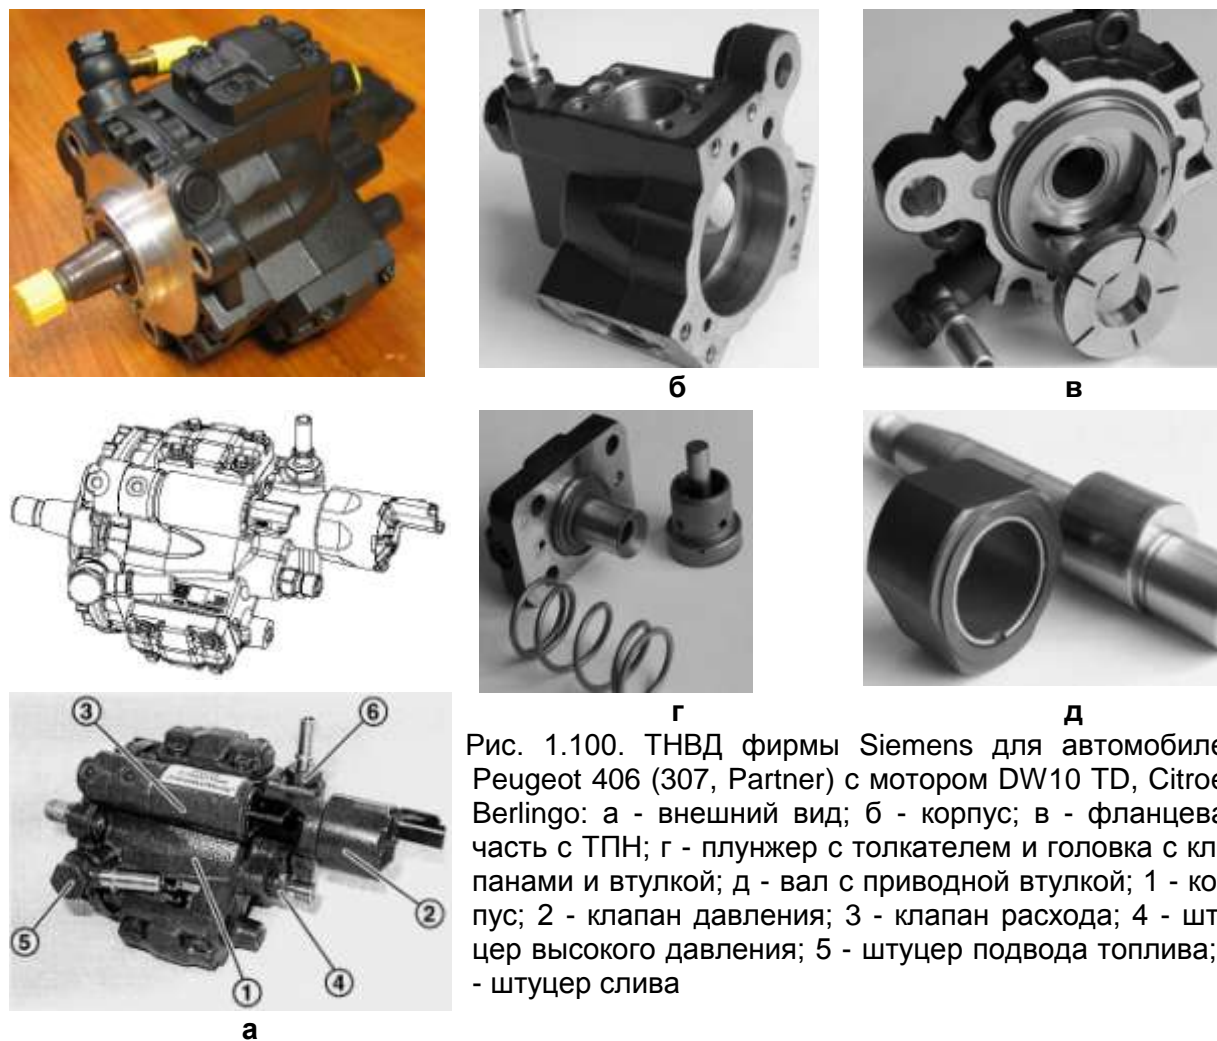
ТНВД фирмы Siemens для автомобилей Peugeot 406 (307, Partner) с мотором DW10 TD, Citroen Berlingo: а - внешний вид; б - корпус; в - фланцевая часть с ТПН; г - плунжер с толкателем и головка с клапанами и втулкой; д - вал с приводной втулкой; 1 - корпус; 2 - клапан давления; 3 - клапан расхода; 4 - штуцер высокого давления; 5 - штуцер подвода топлива; 6 - штуцер слива
